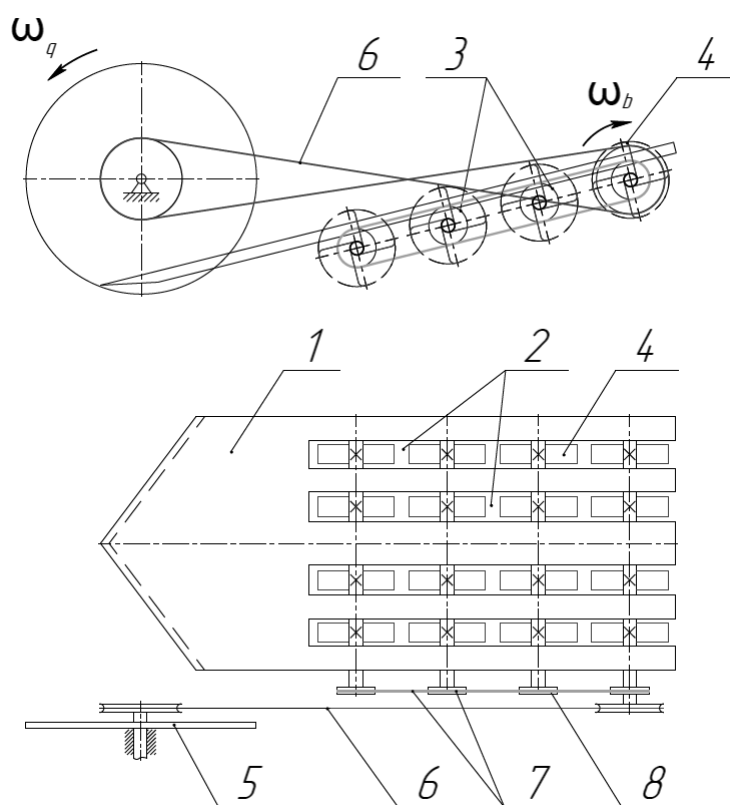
Схема пассивного лемеха с активной рабочей поверхностью
